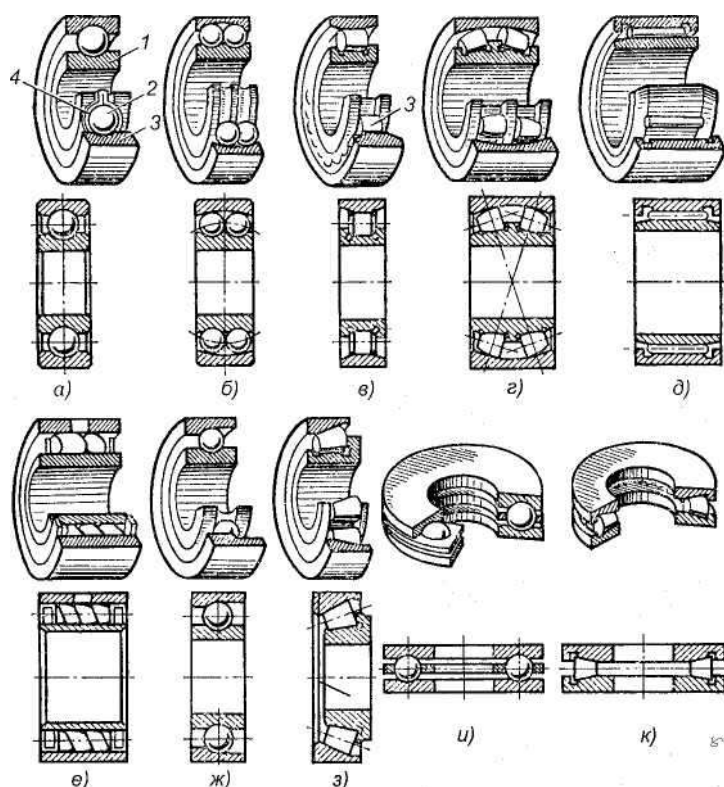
Подшипники качения: а, б, в, г, д, е — радиальные подшипники; ж, з — радиально-упорные подшипники; и, к — упорные подшипники; 1 — внутреннее кольцо; 2 — тело качения; 3 — наружное кольцо; 4 — сепаратор
